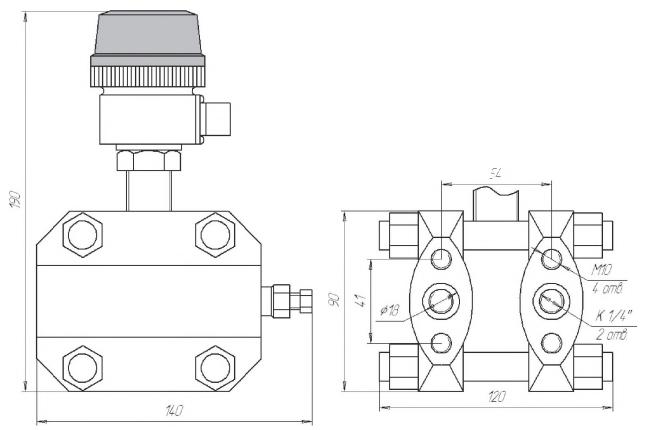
Модель 1168. Нержавеющий корпус, герморазъем.
